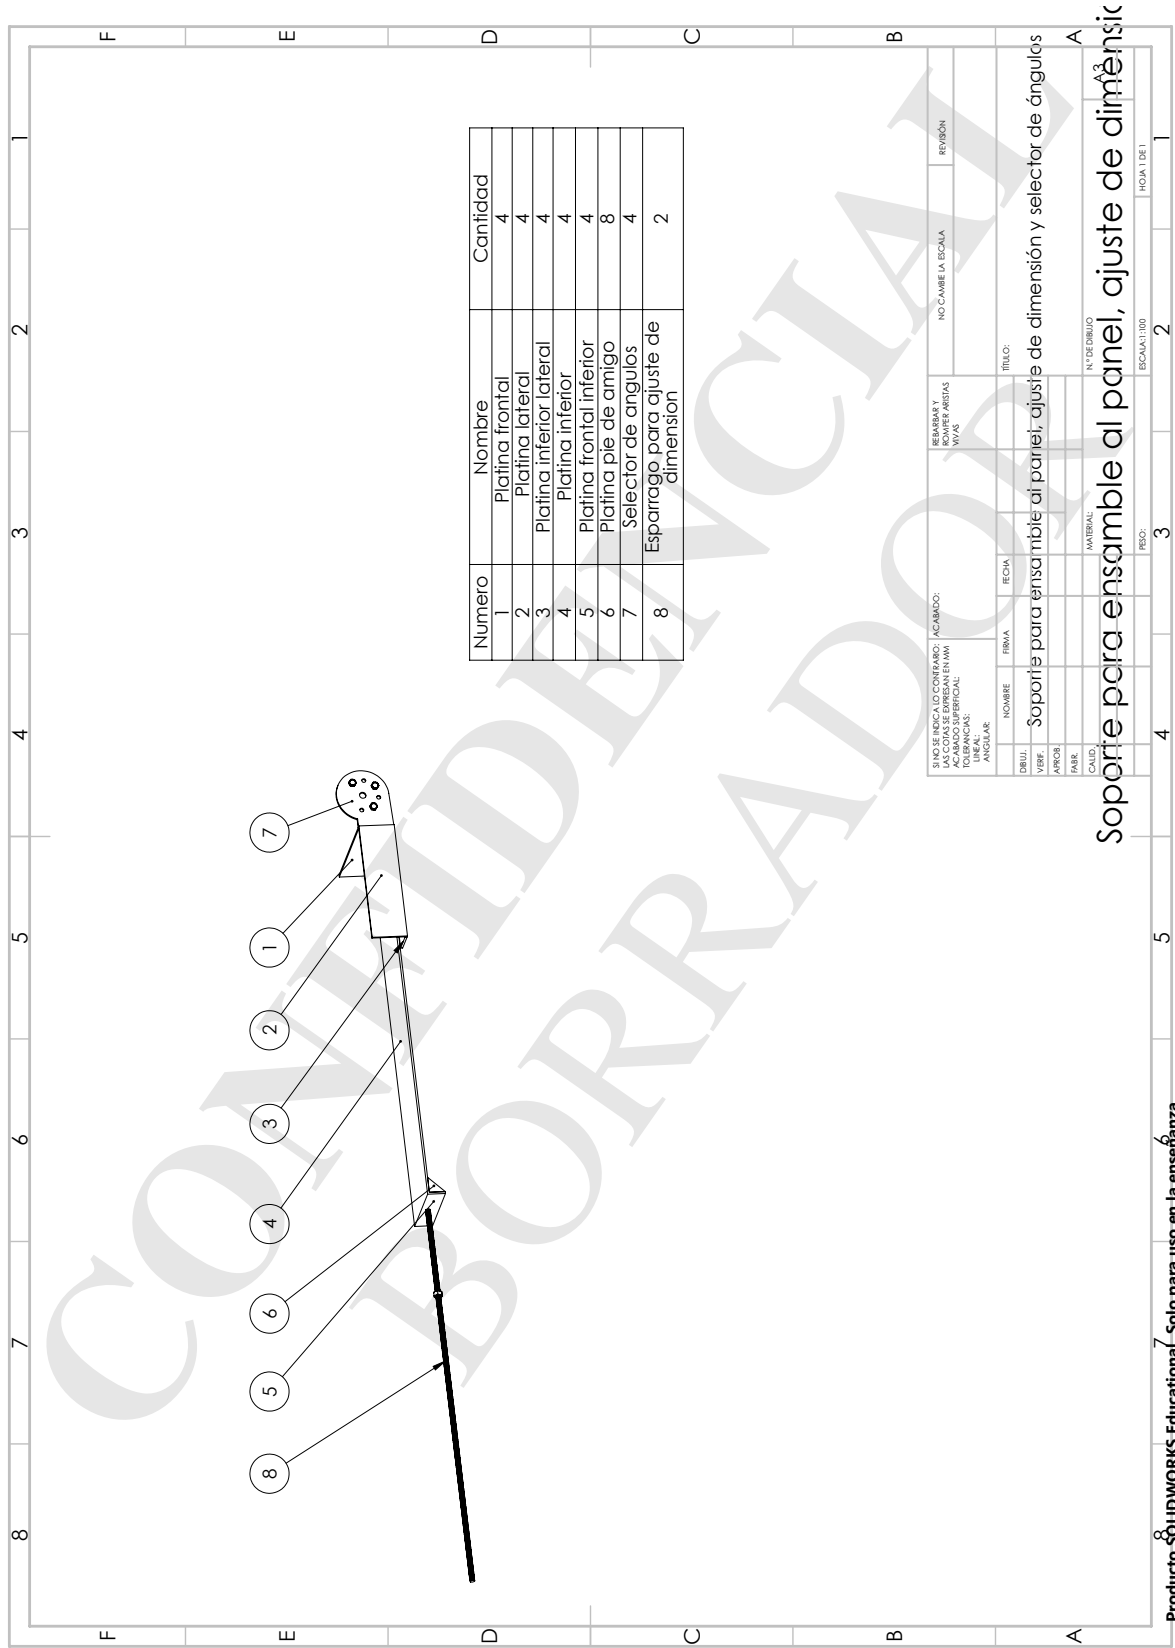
Soporte para ensamble al panel, ajuste de dimension y selector de angulos
